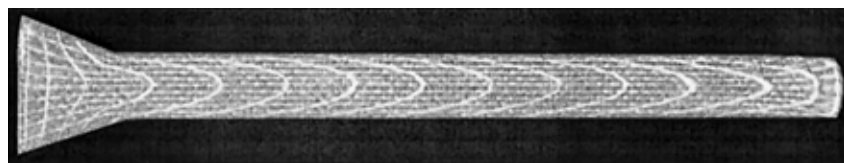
Деформированная сетка, полученная при холодном прессовании цилиндрической заготовки [4]
